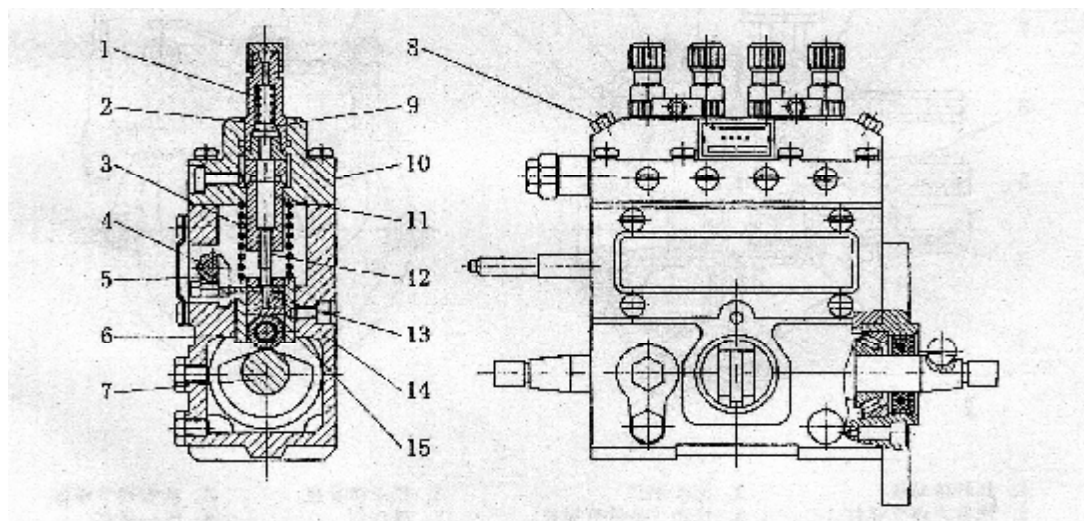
Конструкция инжекторного насоса №1 (4-цилиндровый двигатель)
